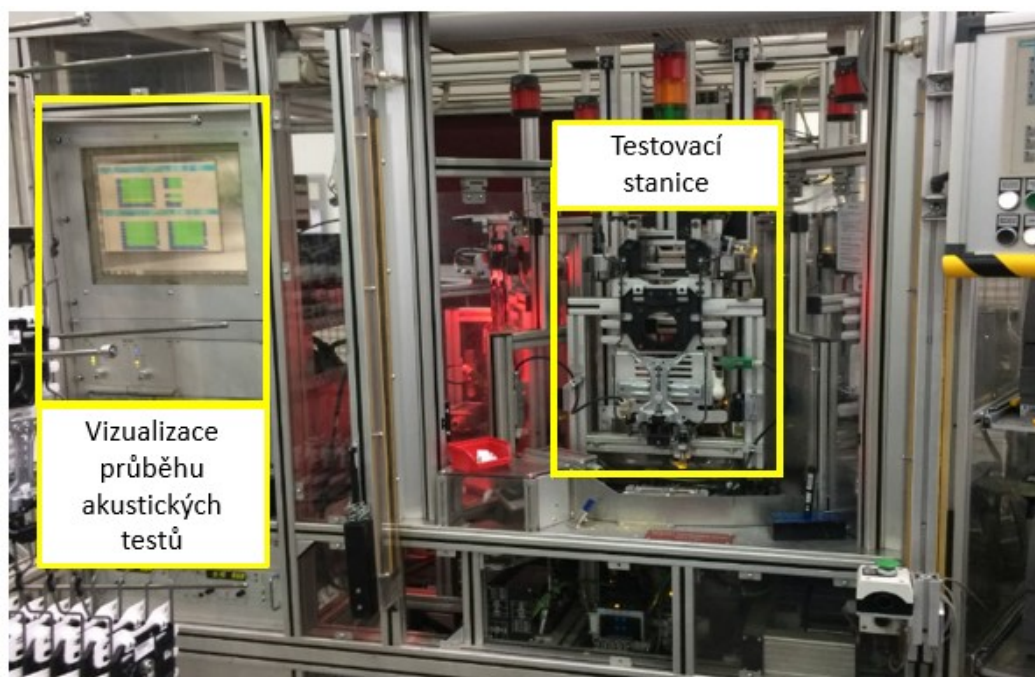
Detail pracoviště AP6, pohled za operátora
